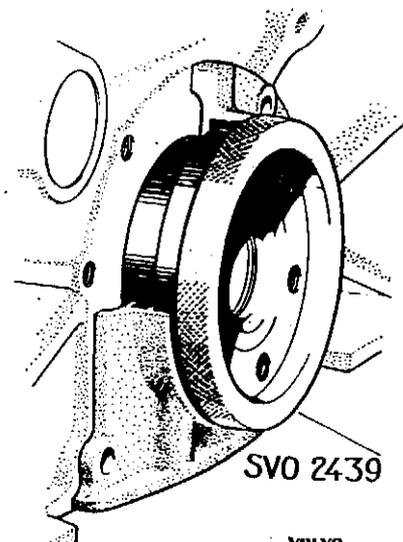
Zentrieren des hinteren Dichtungsflansches
